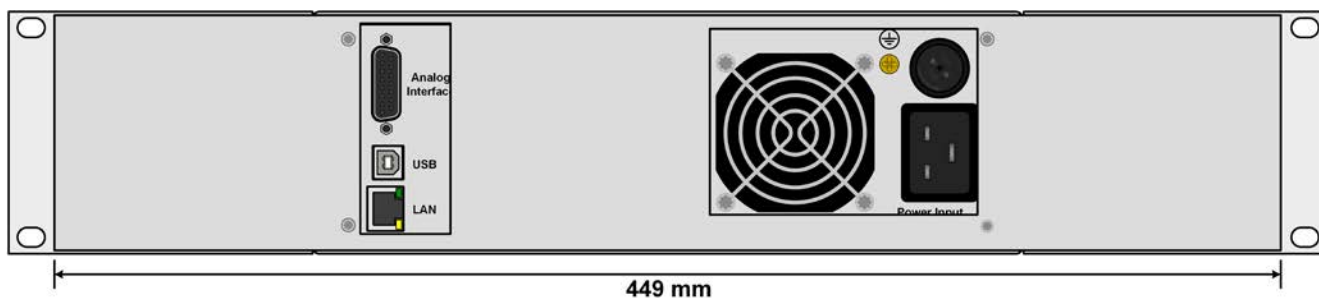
Face arrière après assemblage complet du rack (modèles 1000 W / 1500 W)
